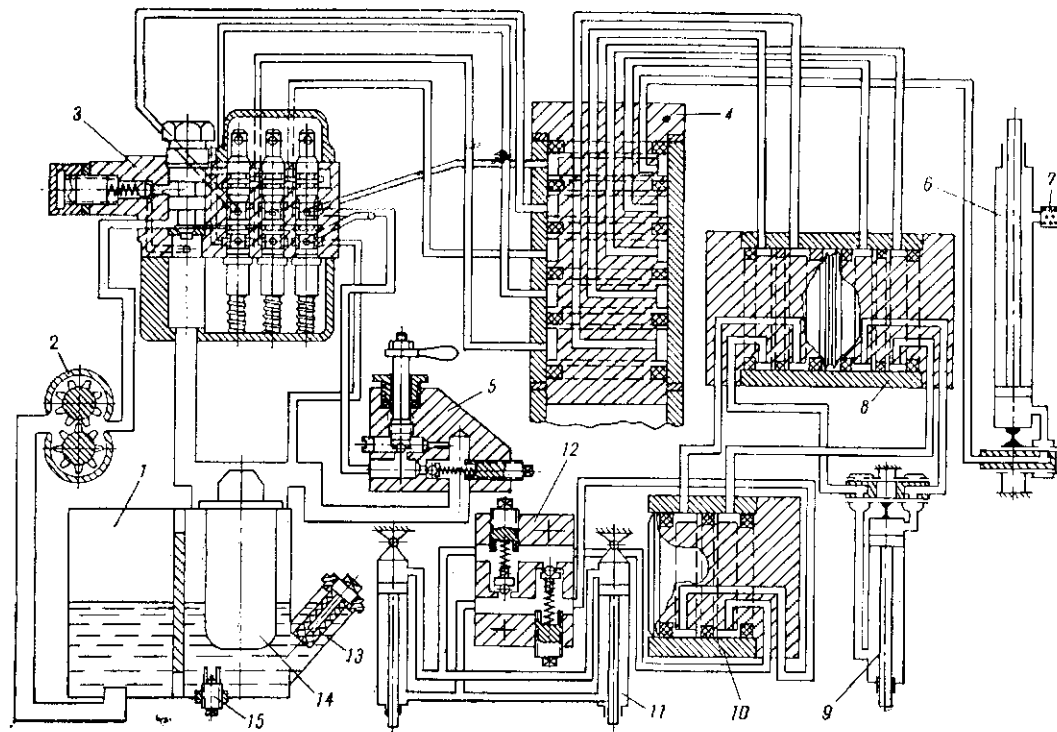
Схема гидравлической системы привода цилиндров подъема стрелы и грейфера погрузчика ПШ-0,4:
